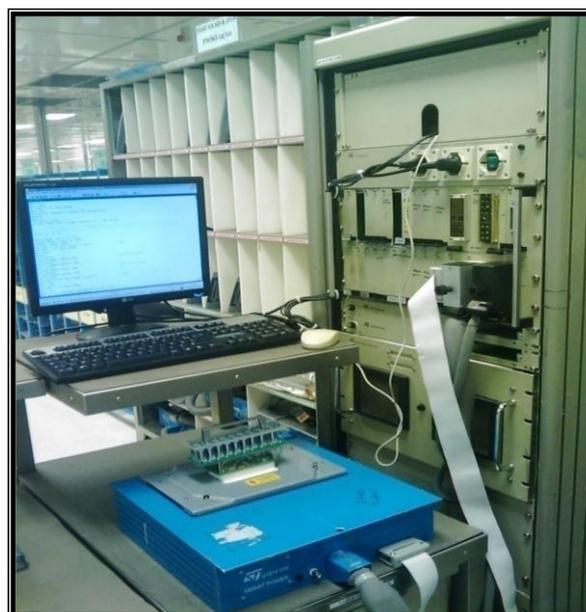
Connexion de l'AutoJig au Test-Head et au Testeur
